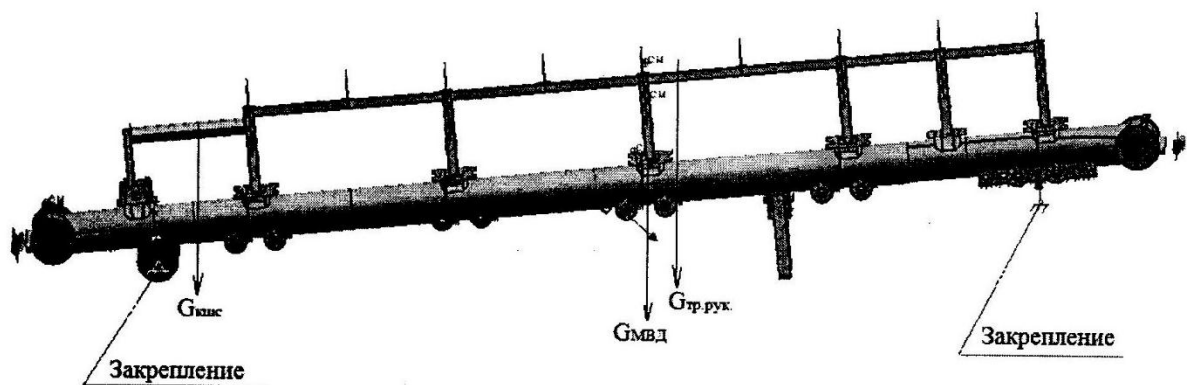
Схема нагружения и закрепления несущей конструкции;
